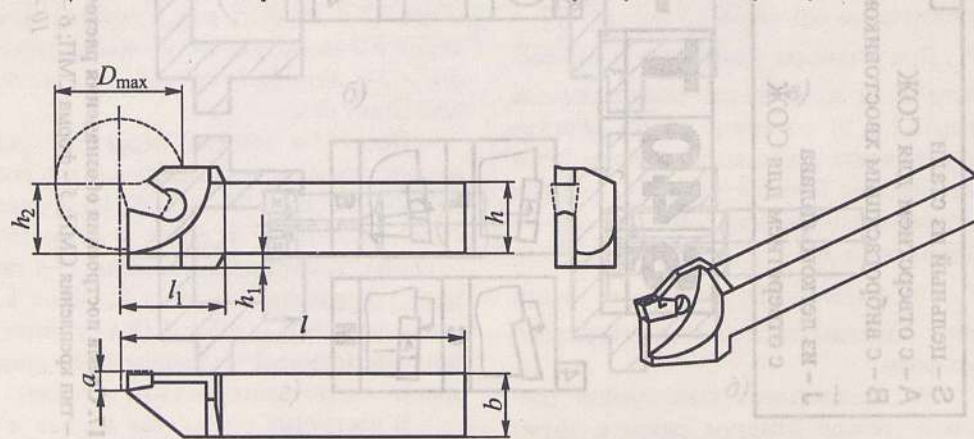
Отрезной резец с клиновым креплением СМП
